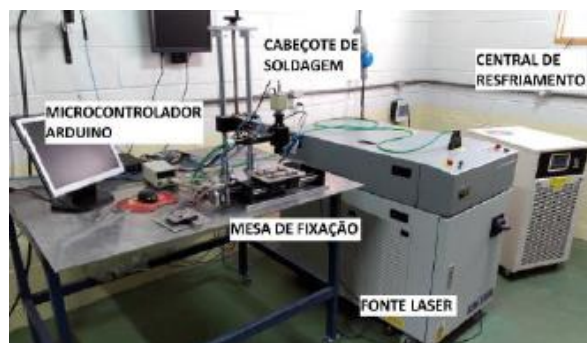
Máquina de soldagem do tipo Nd:YAG da United Winners [13]
